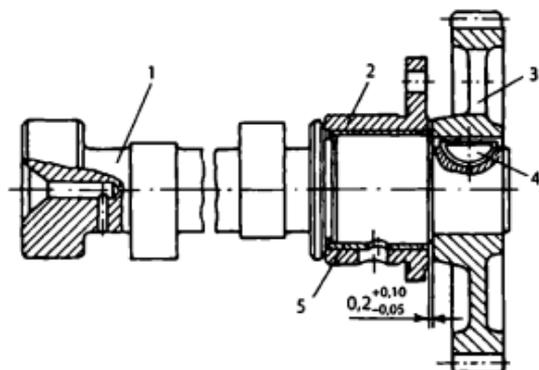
Установлення зазору між шестірнею і вальницею розподільного вала
